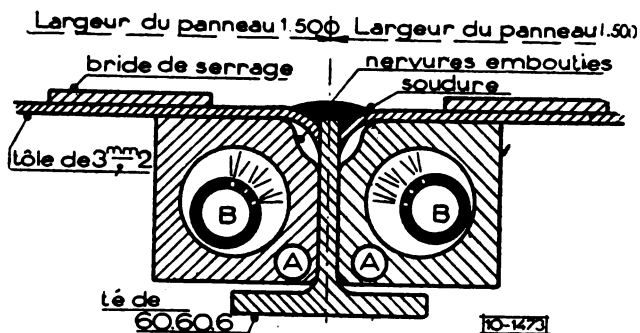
Saldatura di due elementi della parete. A A, forma in due parti; B B, fiamme a gas per il preriscaldamento.
